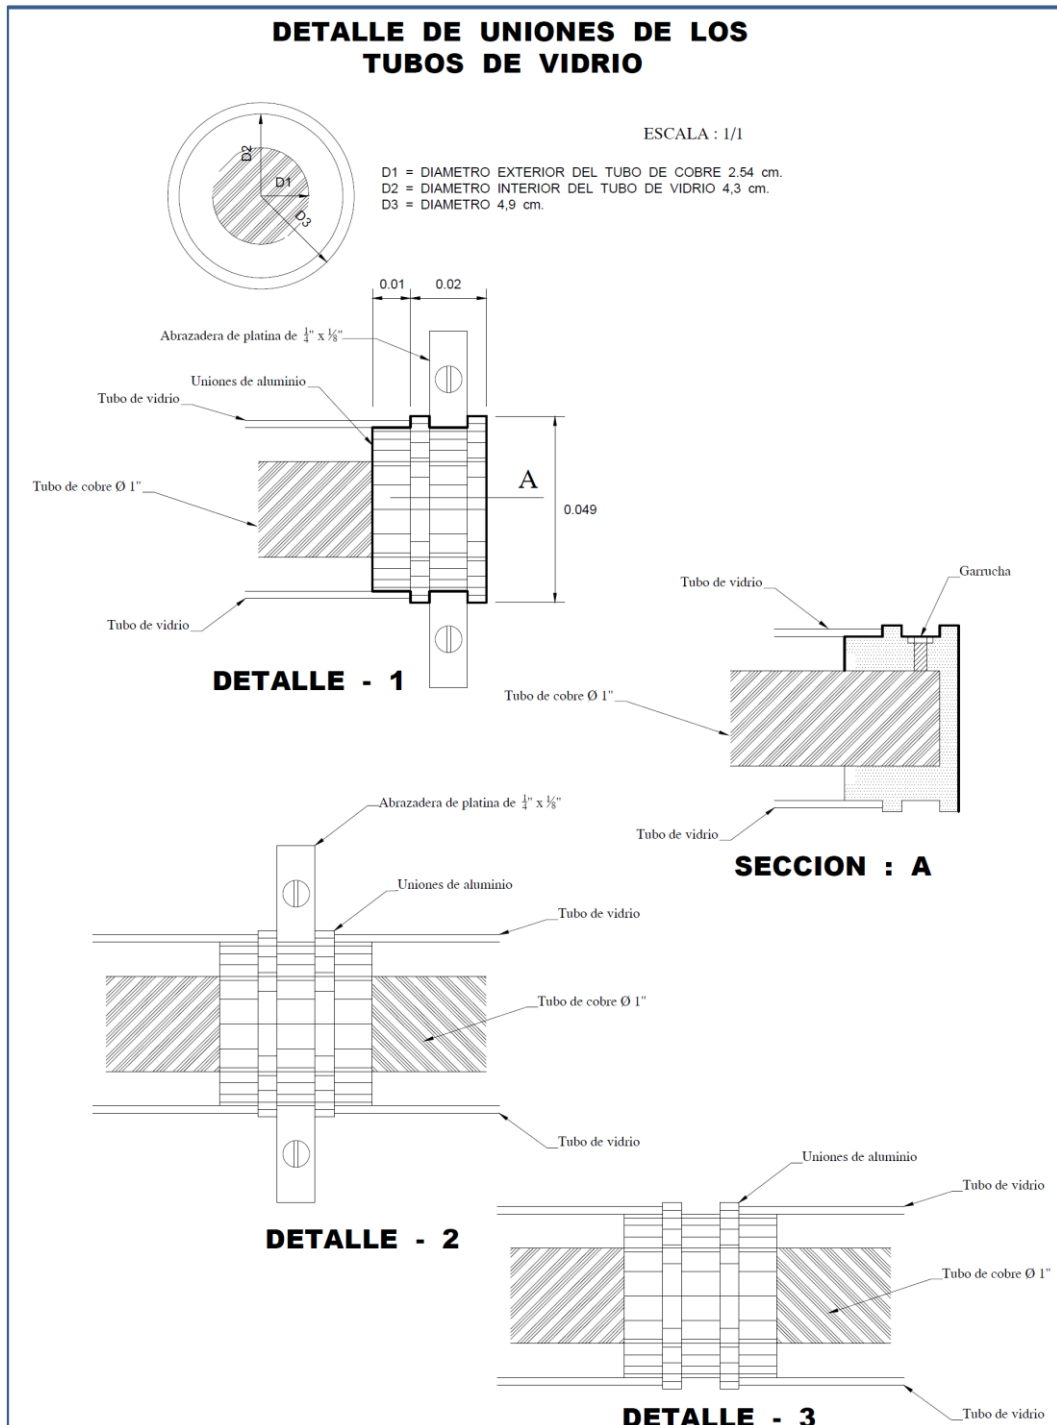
Plano del CCP, detalles de las uniones para los tubos de vidrio
